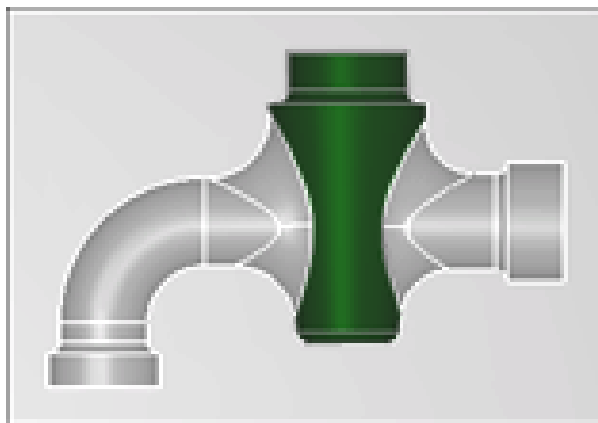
Схема вибору поверхонь фрезерування
